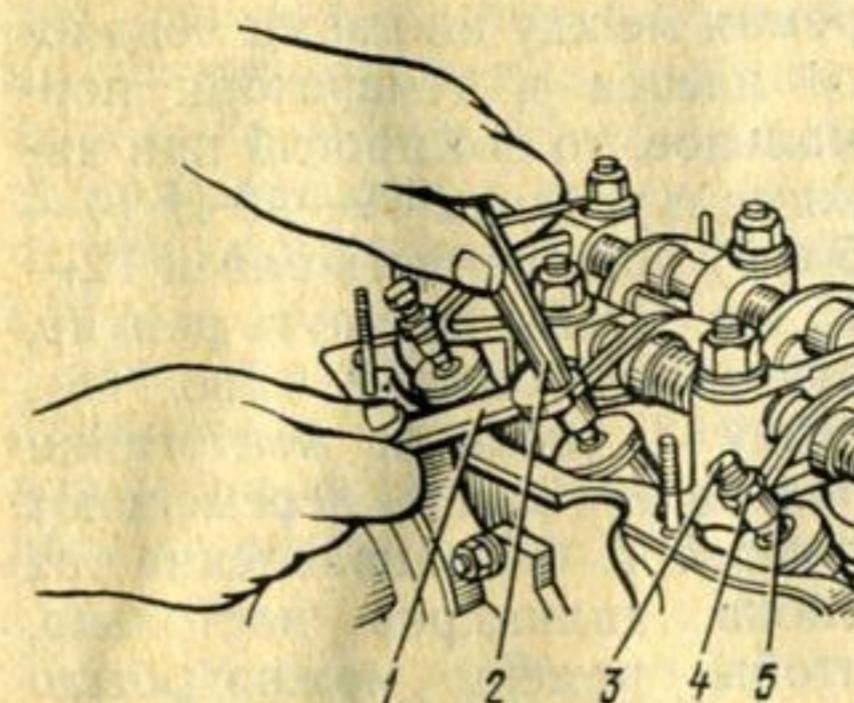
Регулировка зазора между торцами наконечника и стержня клапана:
